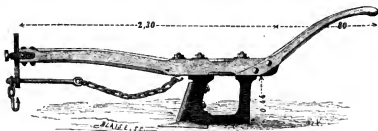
Charrue sous-sol de M. F. Clamageran.
